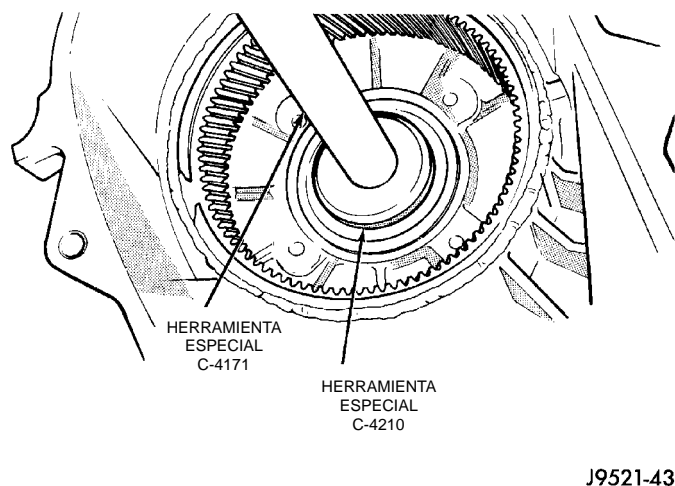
Desmontaje del cojinete del engranaje impulsor
